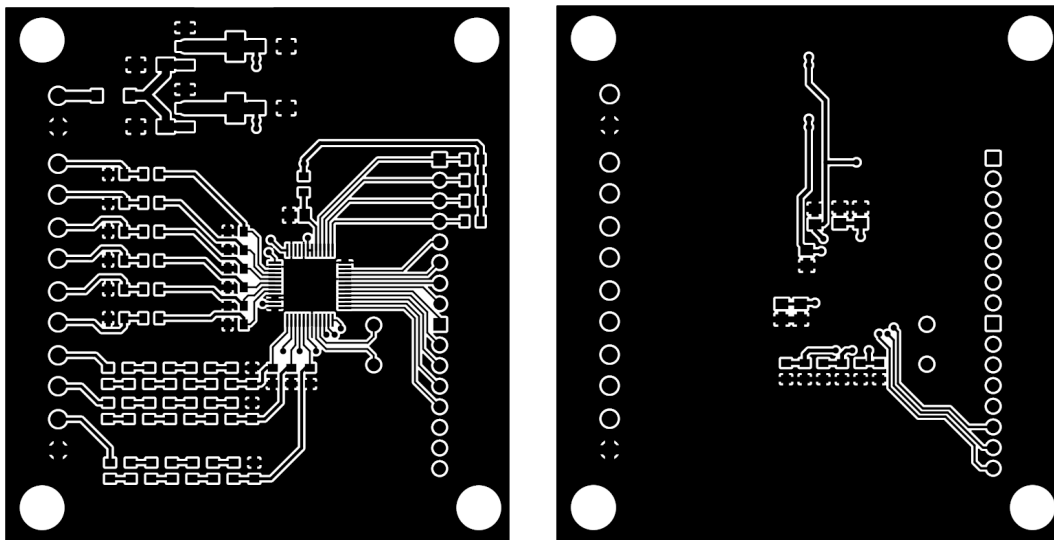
Imágenes gerber PCB V1.0. Fuente propia.
